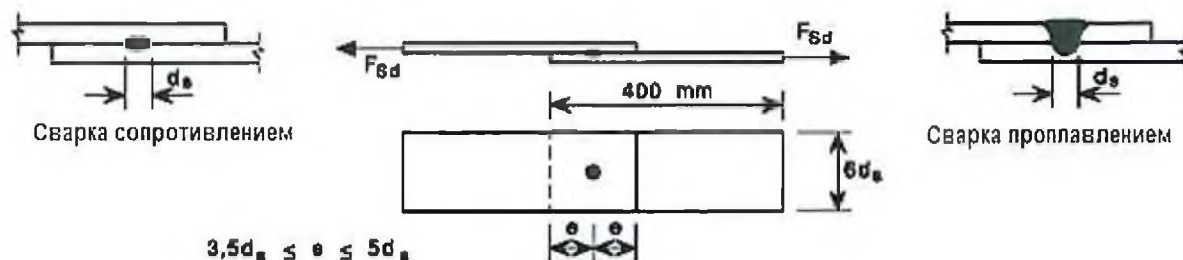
Образцы для испытаний на срез сварных точек
